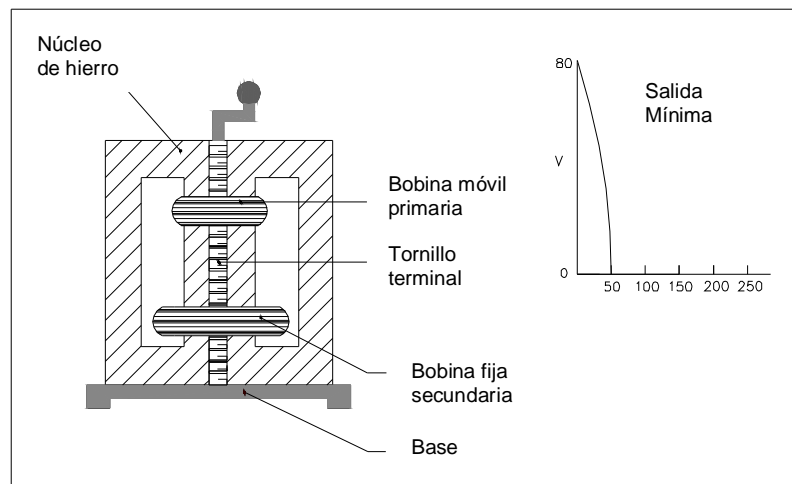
a). - Transformador de CA con bobinas separadas (AMERICAN WELDING SOCIETY, Manual de soldadura, Tomo I, Pág. 20)
